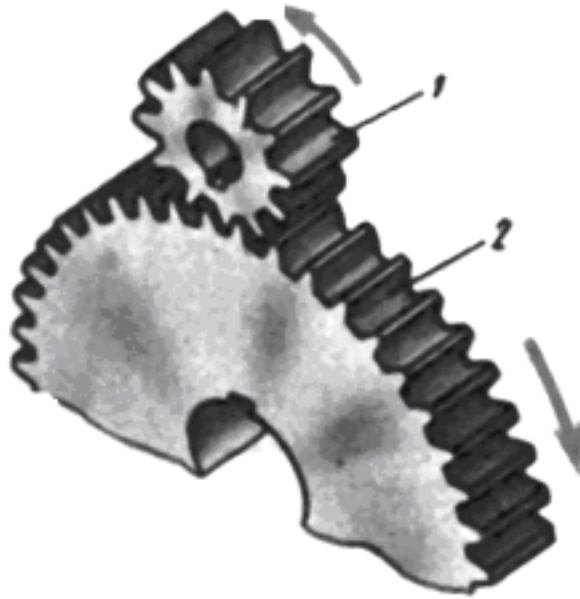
Циліндрична прямозуба зубчаста передача:
